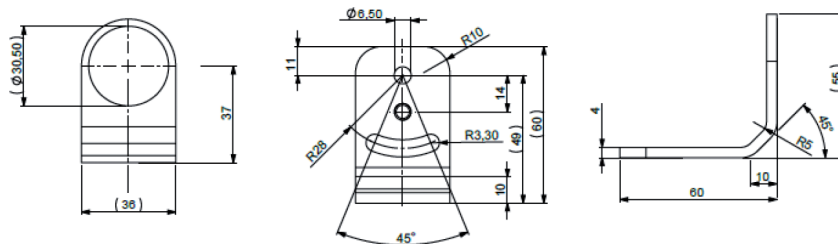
Montagewinkel, justierbar in einer Achse, mit Stativgewinde
